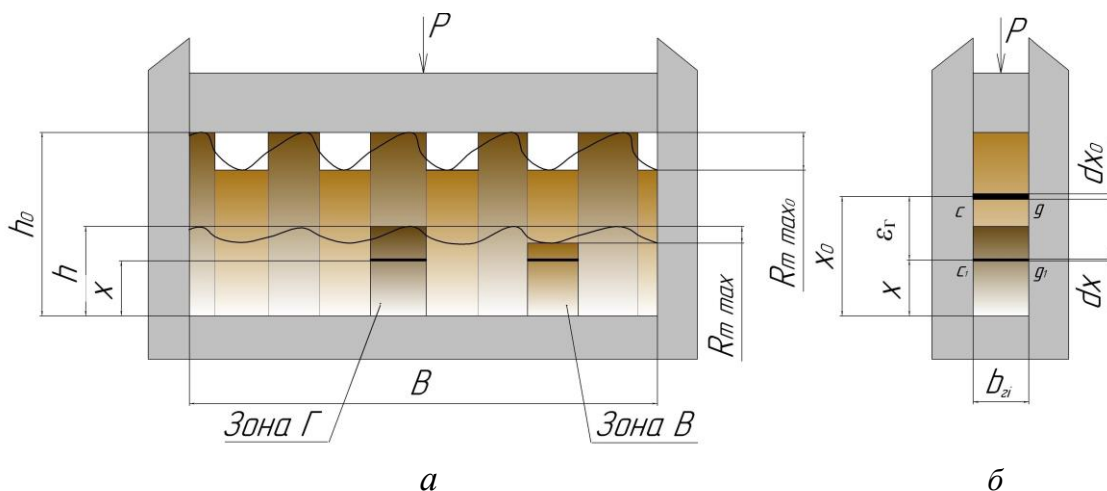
Расчетная схема: а – упрощенная схема заготовки; б – схема прессования гребня
